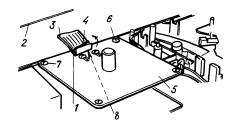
Снятие двигателя привода диска: I — разъем устанавливается с разомкнутым штырьком 1; 2 — печатная плата управления, 3 — двенадцатиполюсный разъем, 4 — ослабить фиксирующий рычаг, 5 — прямоприводной двигатель, 6 — винт крепления, 7 — пружинная шайба; 8 — двенадцатиполюсный разъем
